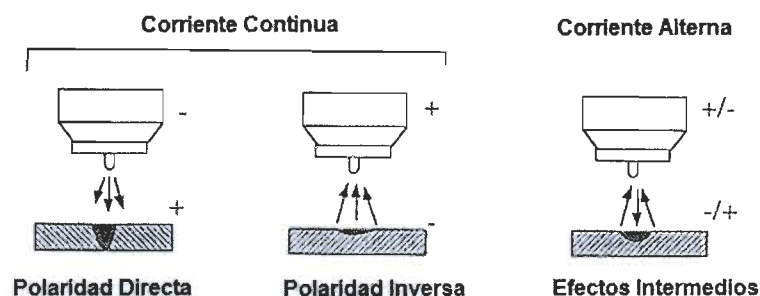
Características de tipos de corriente para soldadura GTAW (15).
